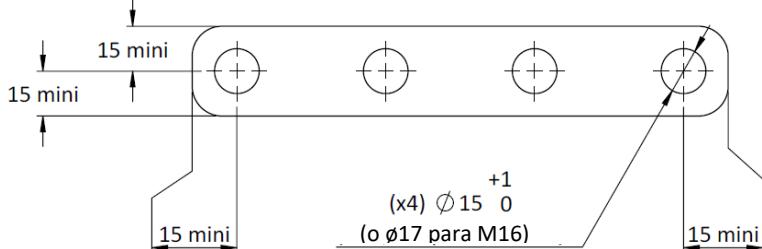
Plano de montaje autorizado para la pletina baja no perforada
